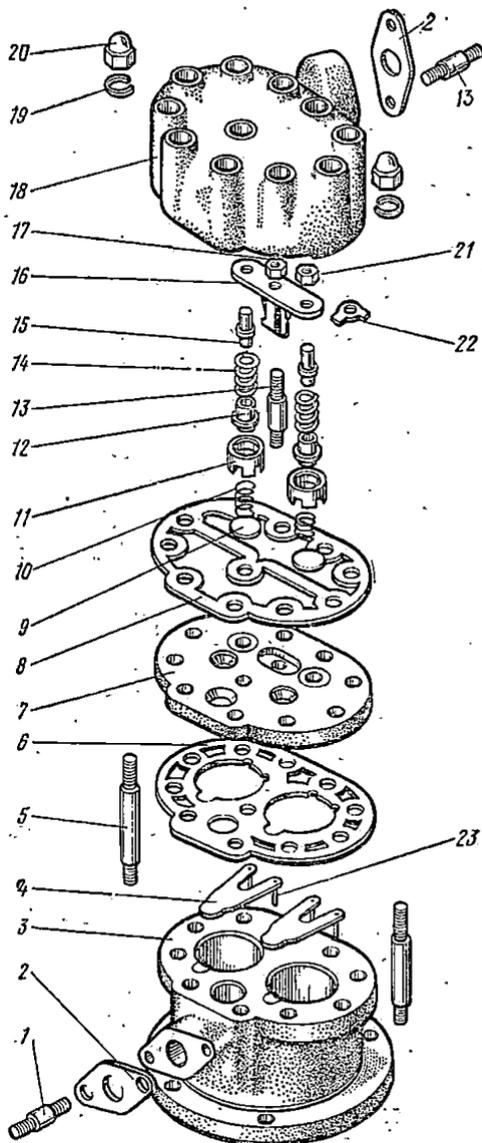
Головка блока, клапанная группа и блок цилиндров компрессора 2ФВ4/4,5:
